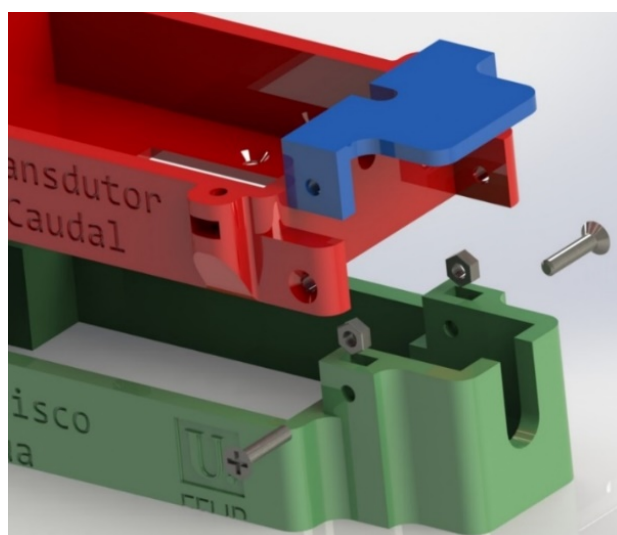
Vista explodida da montagem entre a base, a caixa da eletrónica e a tampa lateral
